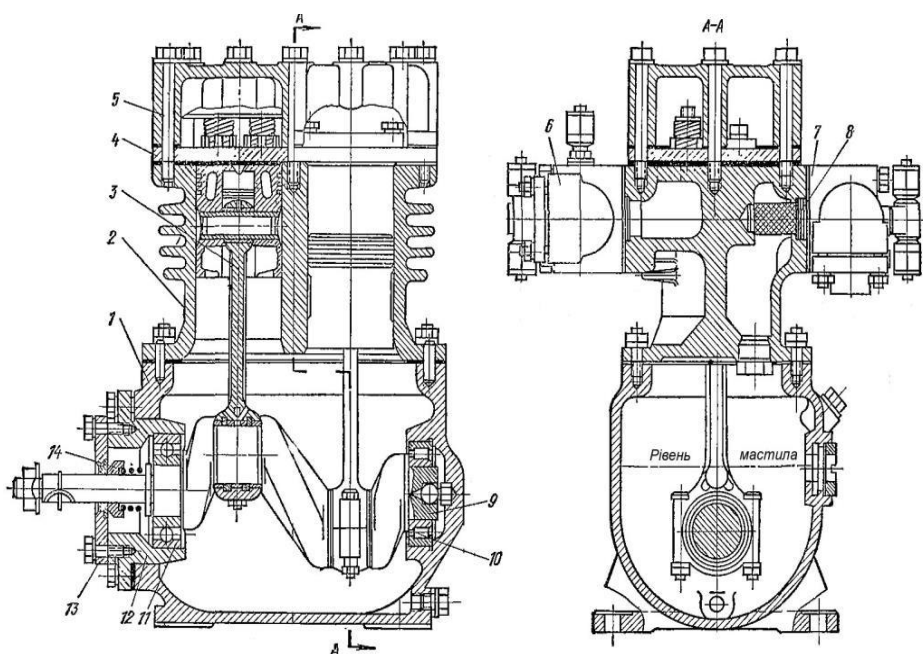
Конструкція фреонового компресора ФВ-6.
